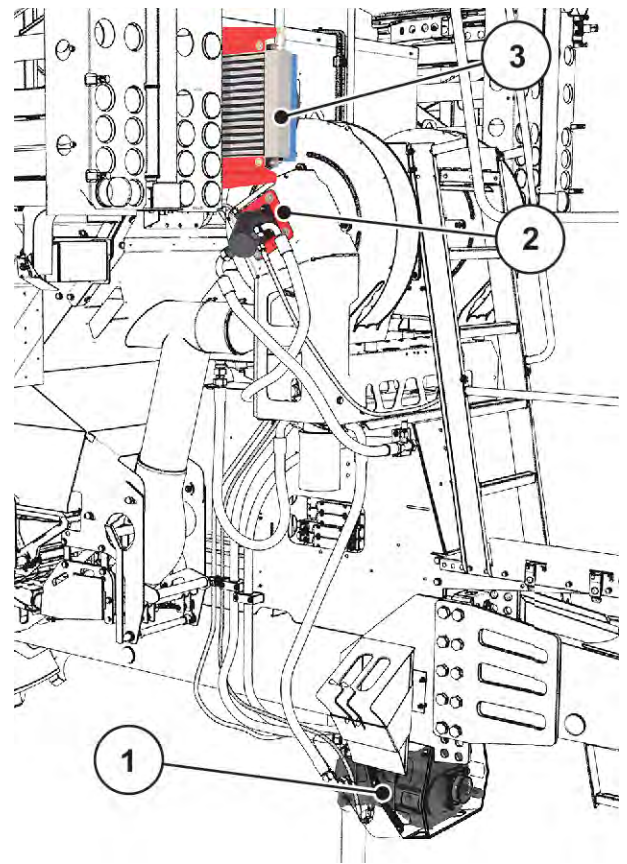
Contrôle de la pompe à piston axial, du moteur à piston axial et du refroidisseur d'huile
